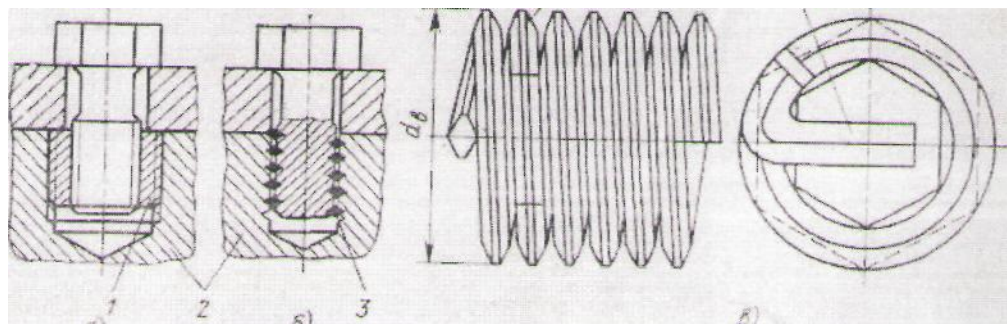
Схемы завинчивания болта в корпус из легкого сплава с применением втулки и упругой вставки
